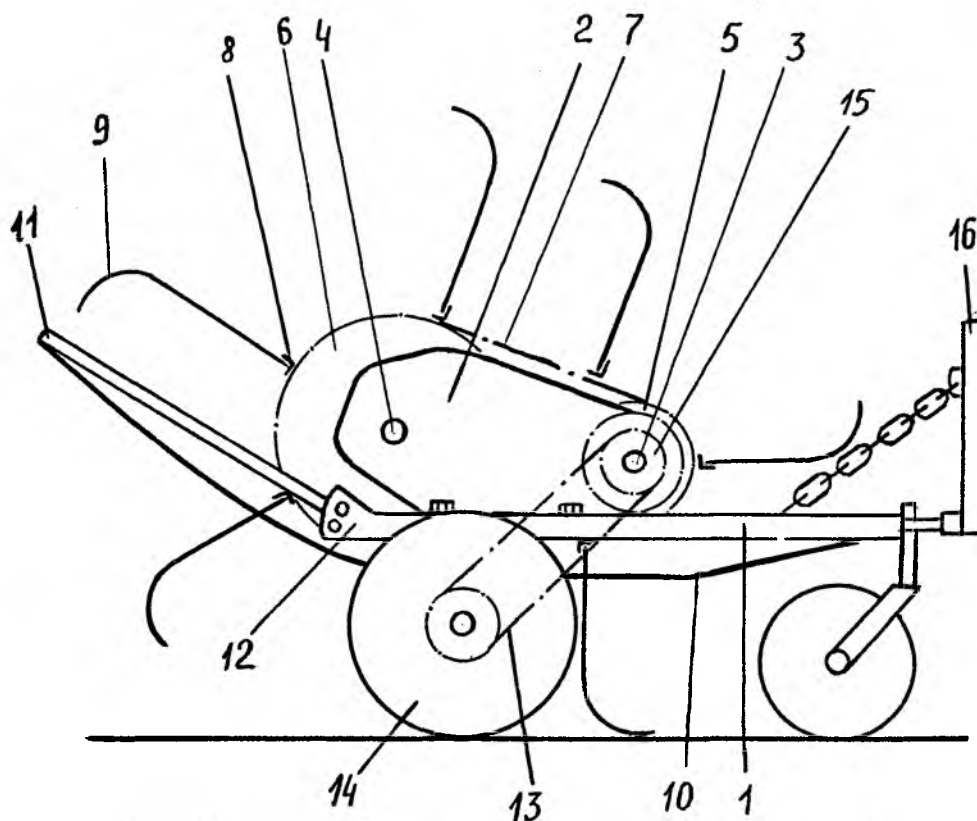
Схема ворошилки лент льна: 1 – рама; 2 – съёмный корпус; 3, 4 – вал; 5, 6, 15 – звёздочка; 7 – цепь; 8 – планка; 9 – зуб; 10 – обечайка; 11 – рычаг; 12 – сектор; 13 – цепная передача; 14 – колесо; 16 – рама навески
